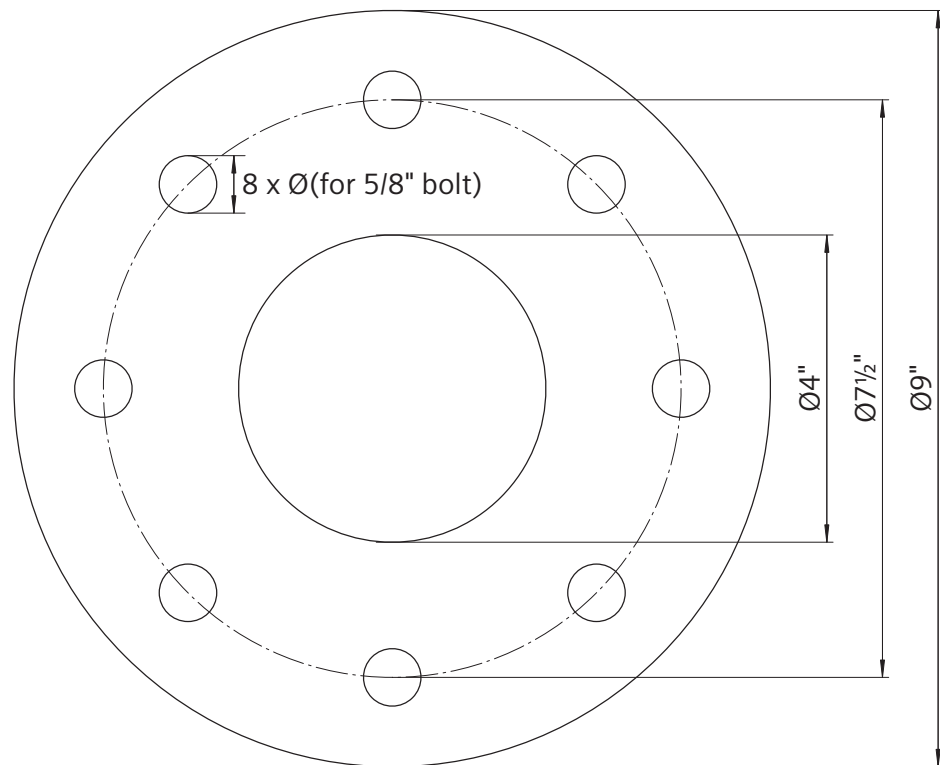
Dimensioni della flangia ANSI 4"/150 lbs.
